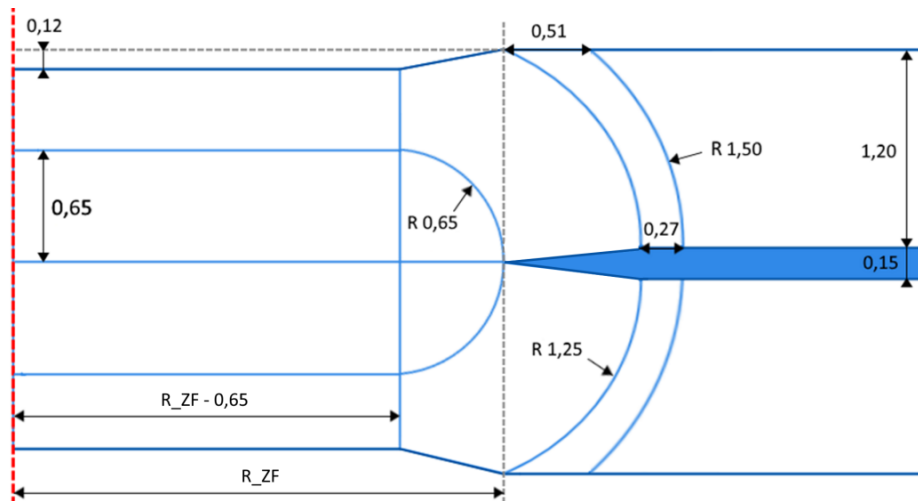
Géométrie de soudure modélisée, avec les dimensions données en mm
